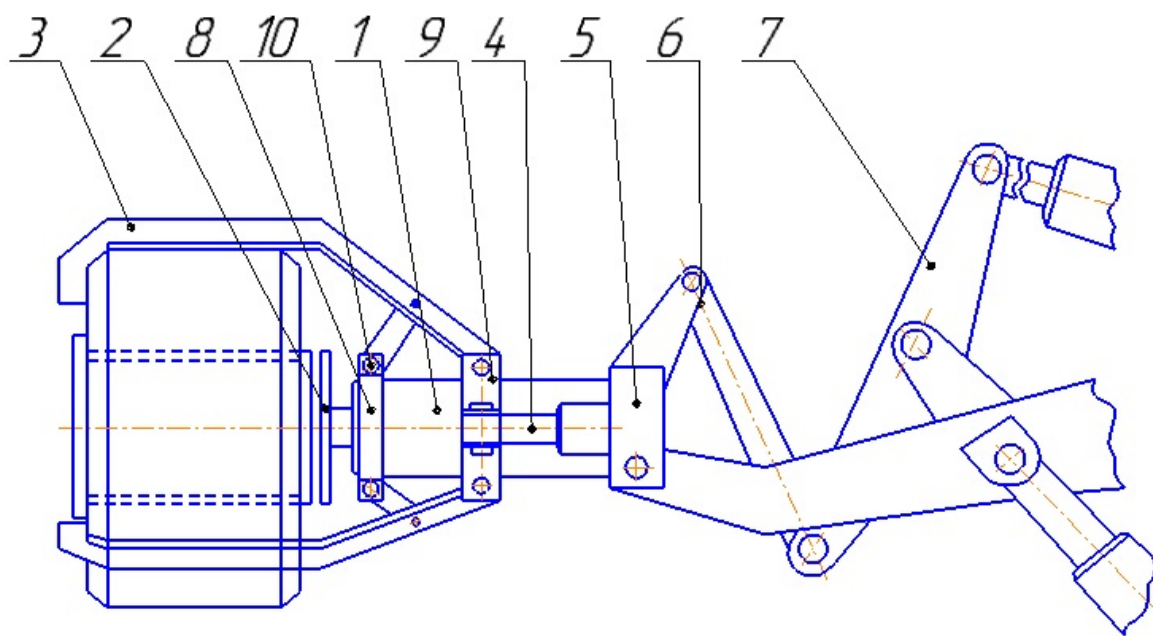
Приспособление на фронтальный погрузчик для монтажа и демонтажа колес и шин
